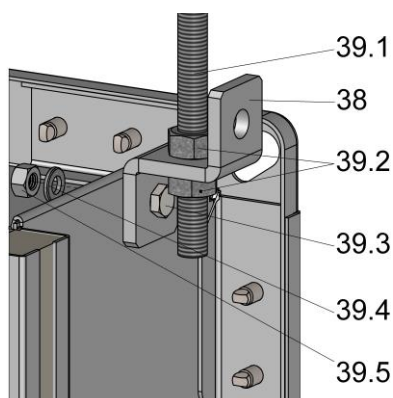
dettaglio fissaggio (posizione pala serranda orizzontale)
